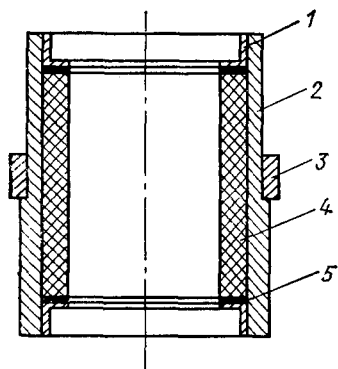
Схема приспособления для пайки керамики с металлическими манжетами
